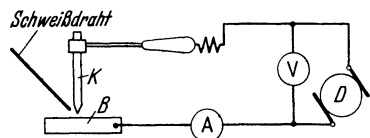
Grundform einer Lichtbogenschweißanlage.
